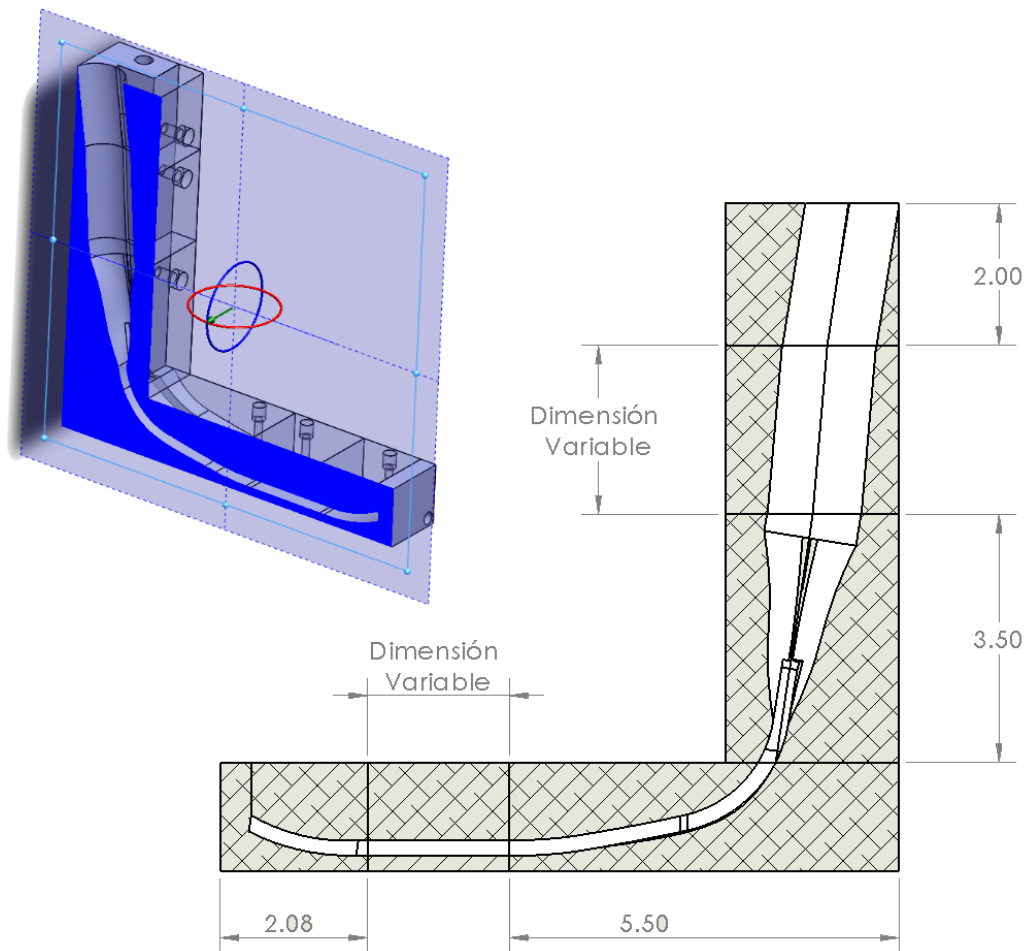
Molde superior seccionado explicando la dimensión variable
